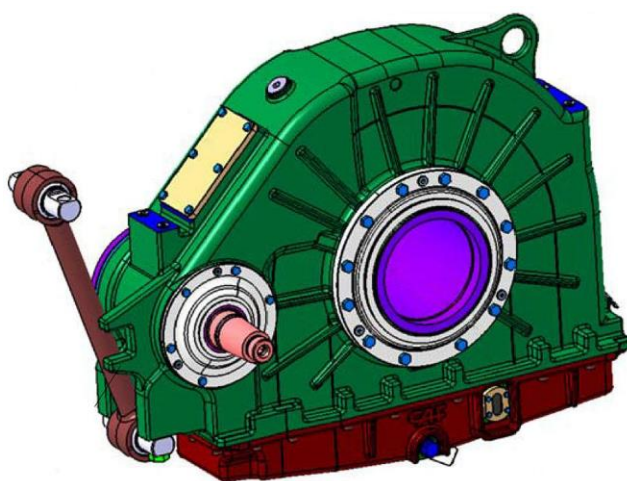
Редуктор на оси колесной пары Рис. 90. Редуктор с реактивной тягой подвески
